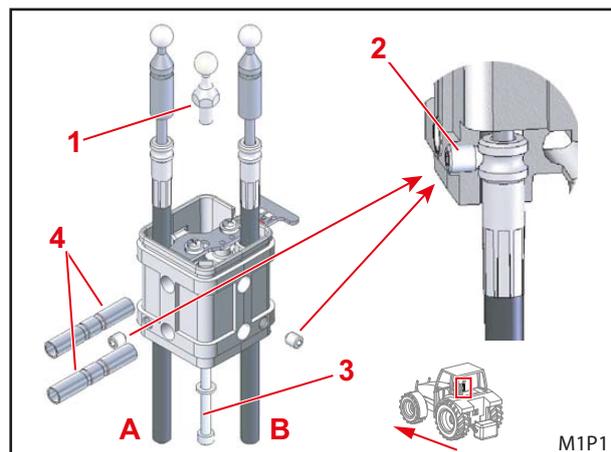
Montaggio dei cavi Bowden – Fase 2
